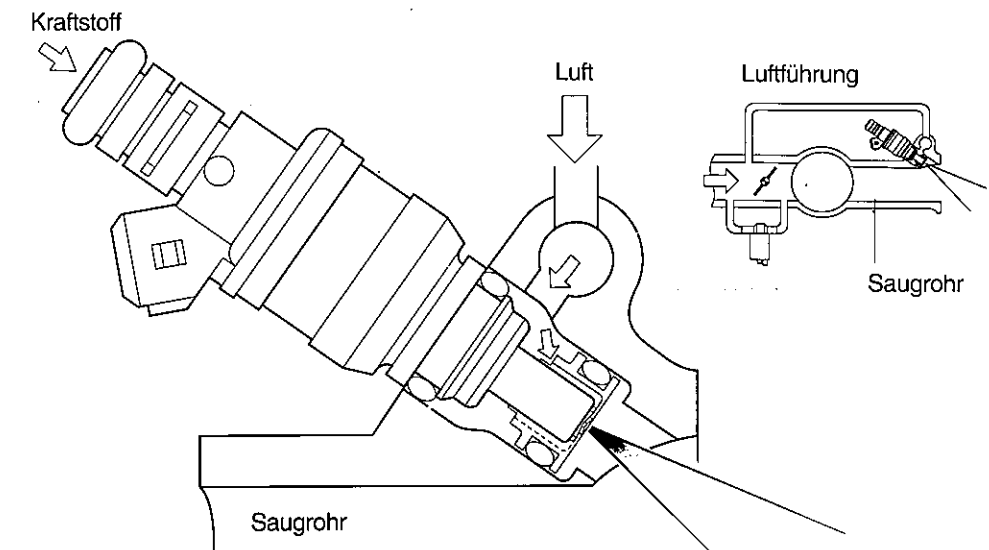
Einspritzventil mit Luftumfassung (Bosch-Pressebild 7934)
